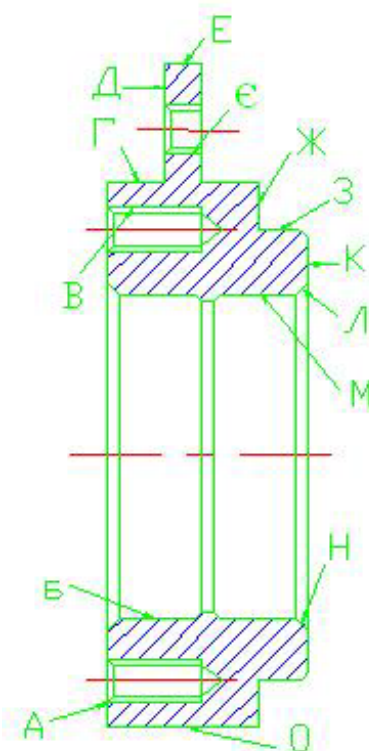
Ескіз стакану ВС185х250.07-00-05 з позначеними оброблюваними поверхнями.
